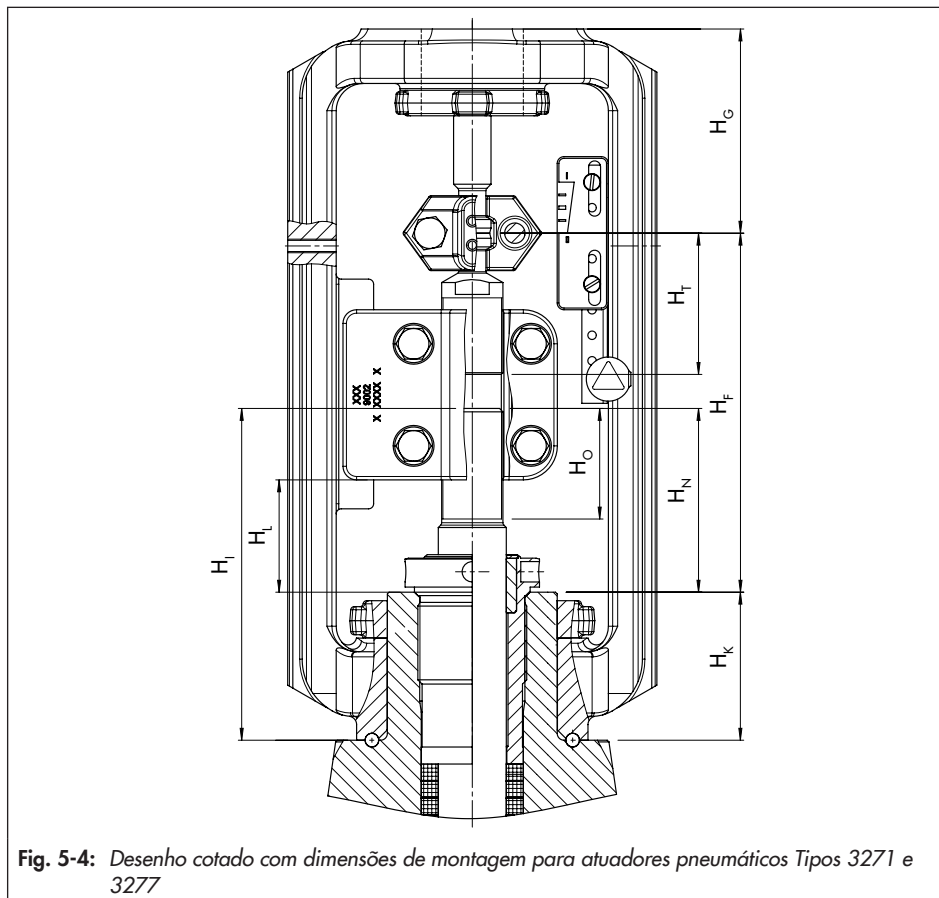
Desenho cotado com dimensões de montagem para atuadores pneumáticos Tipos 3271 e 3277
